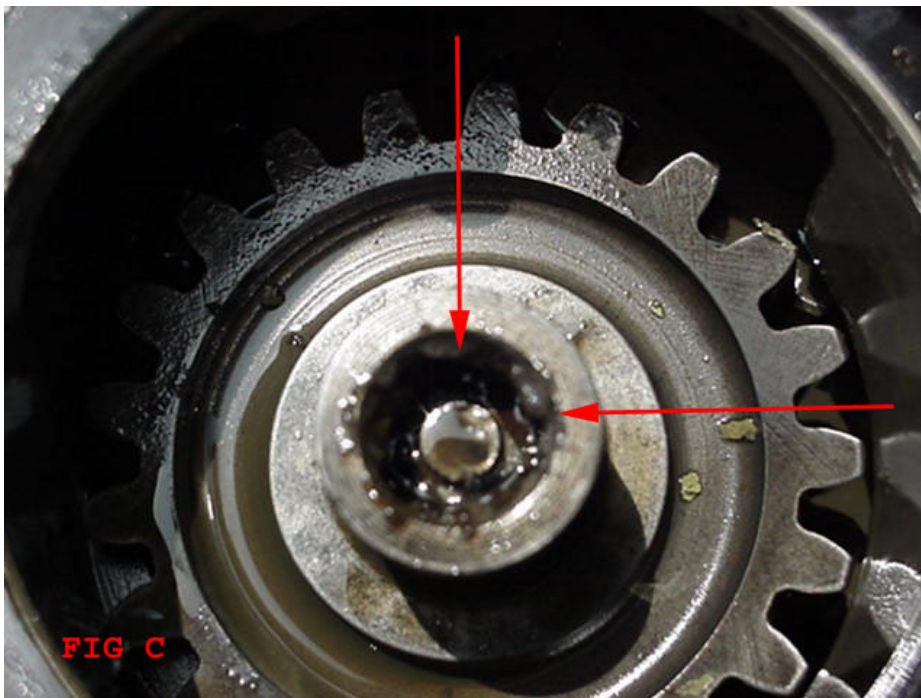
FIG C detalle del coupling roto dentro del engranaje de la caja de accesorios.
